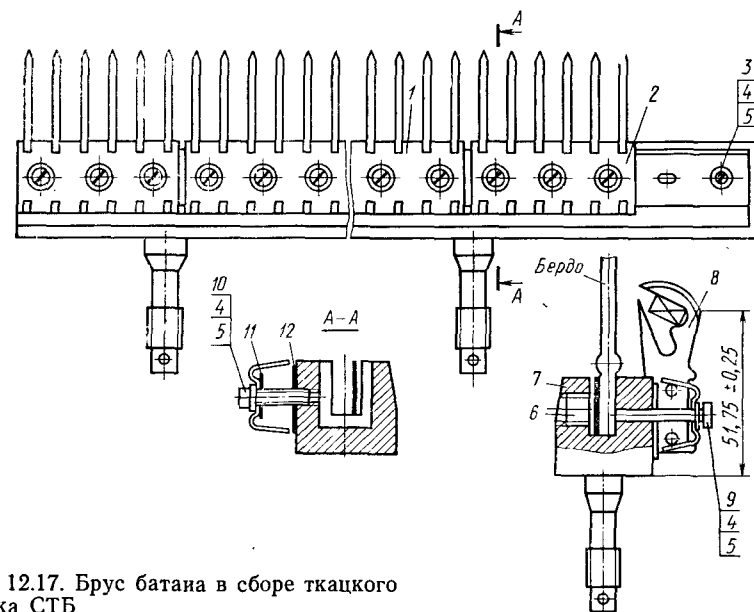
Брус батана в сборе ткацкого станка СТБ
